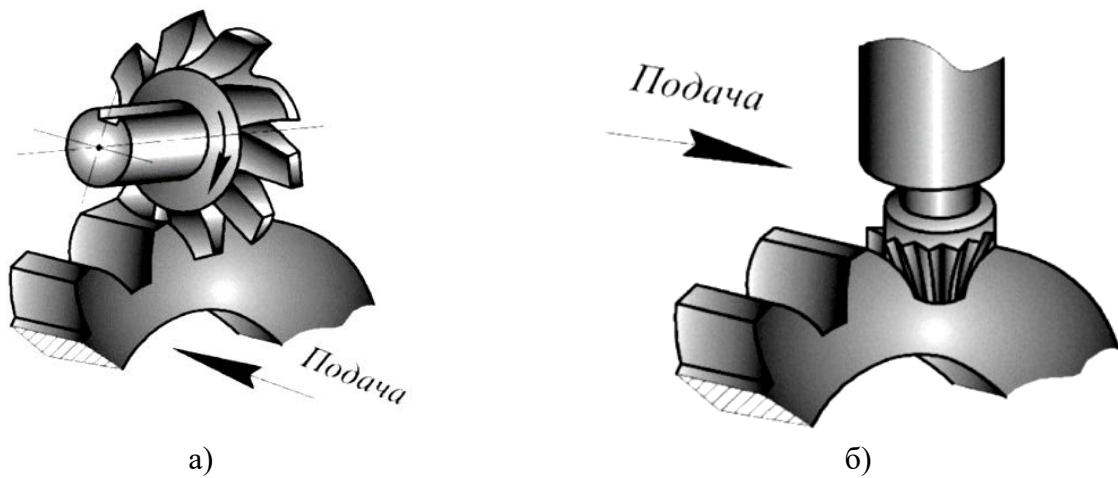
Нарізування зубців методом копіювання: а – дисковою фрезною; б – пальцевою фрезною
